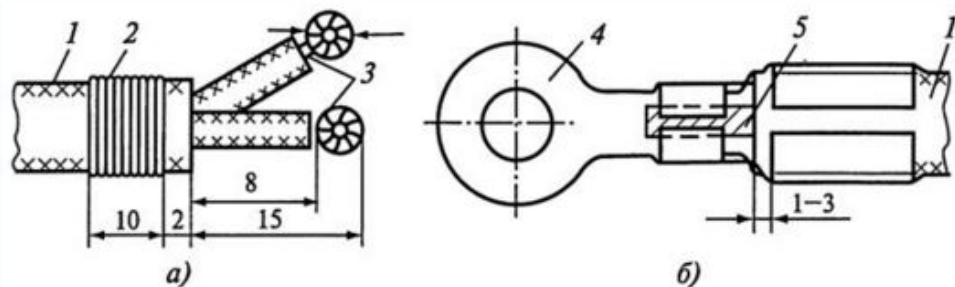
Заделка монтажных проводов кольцами (а) и с помощью кабельного наконечника (б):
